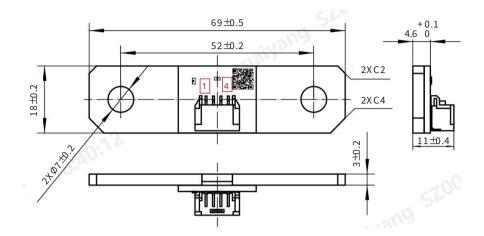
PCBS6918B100P2AC00 电流检测模块结构示意图
